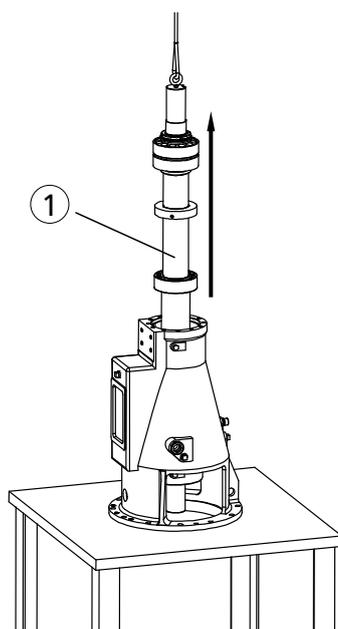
Puxe o conjunto rotativo do conjunto de mancais
